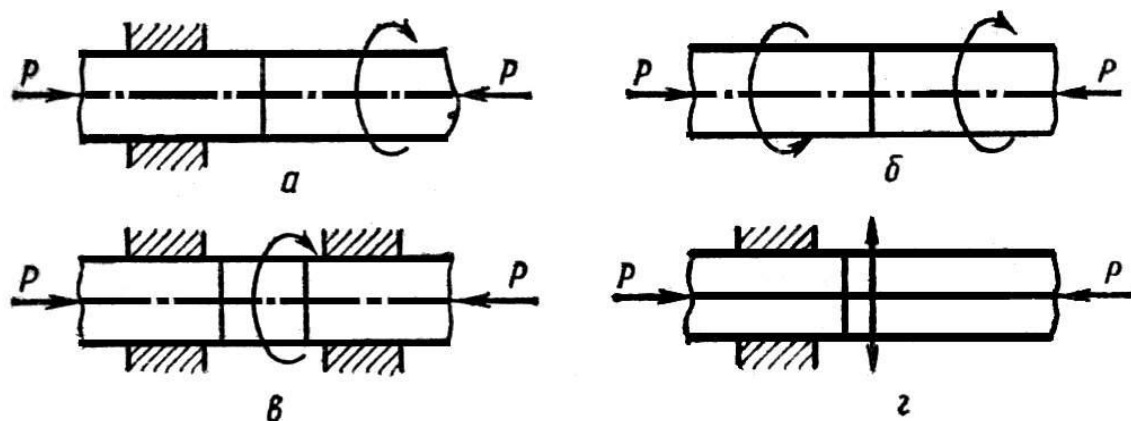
Схема сварки трением: а – при вращении деталей, б – при вращении обеих деталей, в – при неподвижных деталях с вращающейся вставкой, г – при возвратно-поступательном движении одной детали
